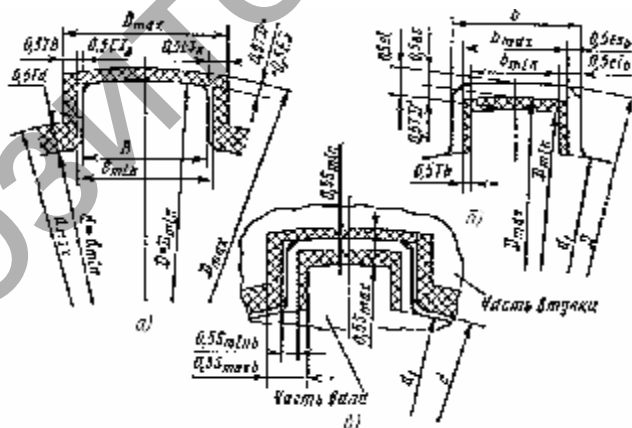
Схема расположения полей допусков прямобоочного шлицевого вала (а), отверстия (б) и соединения (в)
